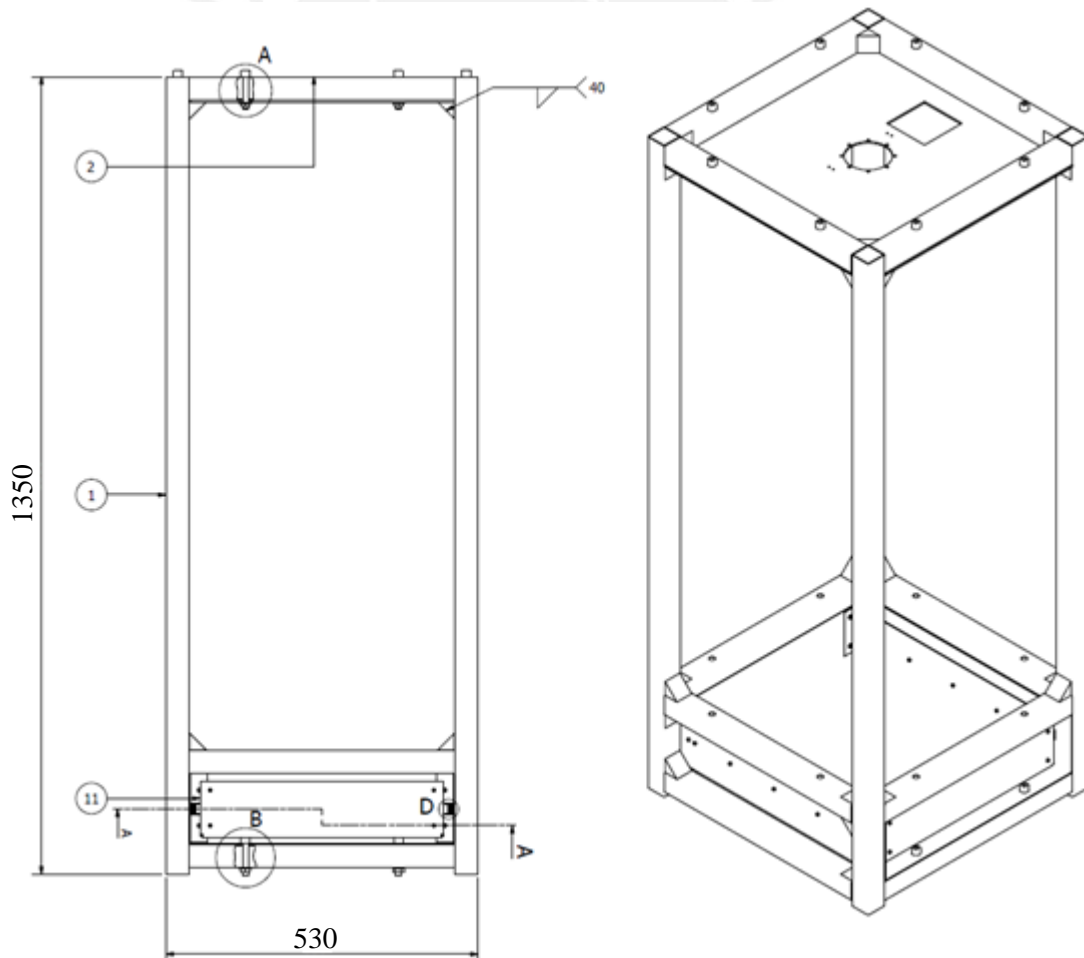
Vista isométrica a la derecha y vista frontal a la izquierda del subensamblaje estructura de soporte. Fuente: Propia.
